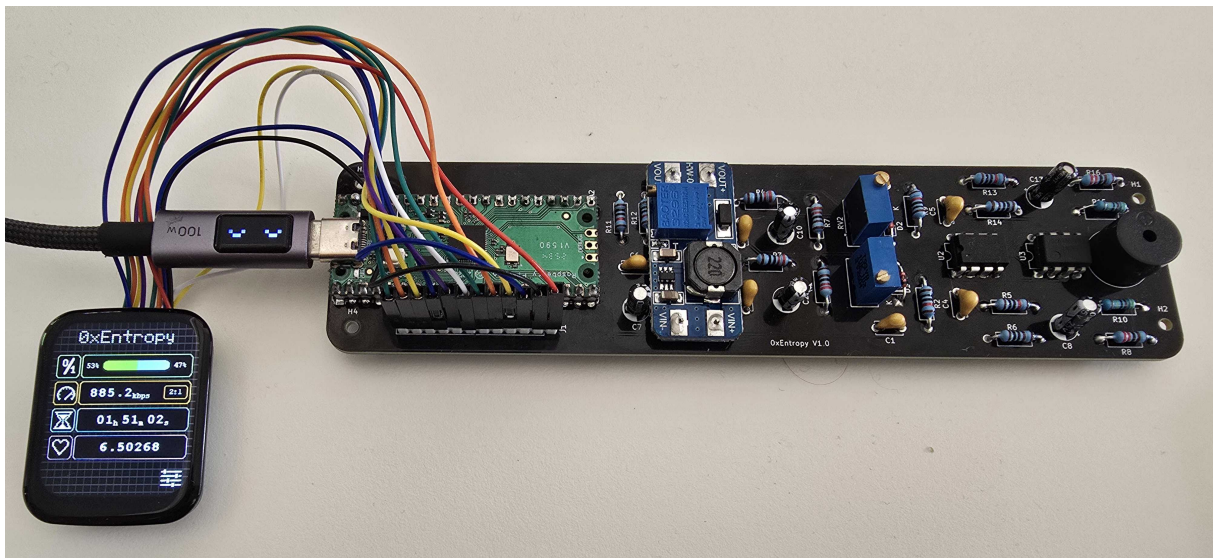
Photographie du circuit imprimé (PCB) finalisé et fonctionnel, avec l'ensemble des composants soudés.
